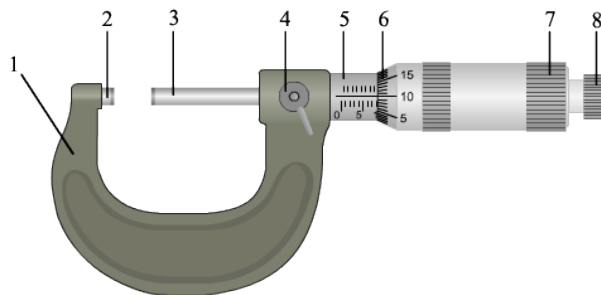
Мікрометр гладкий: 1 – скоба; 2 – п'ятка; 3 – мікрометричний гвинт; 4 – стопор; 5 – стебло; 6 – барабан; 7 – корпус тріскачки; 8 – тріскачка
